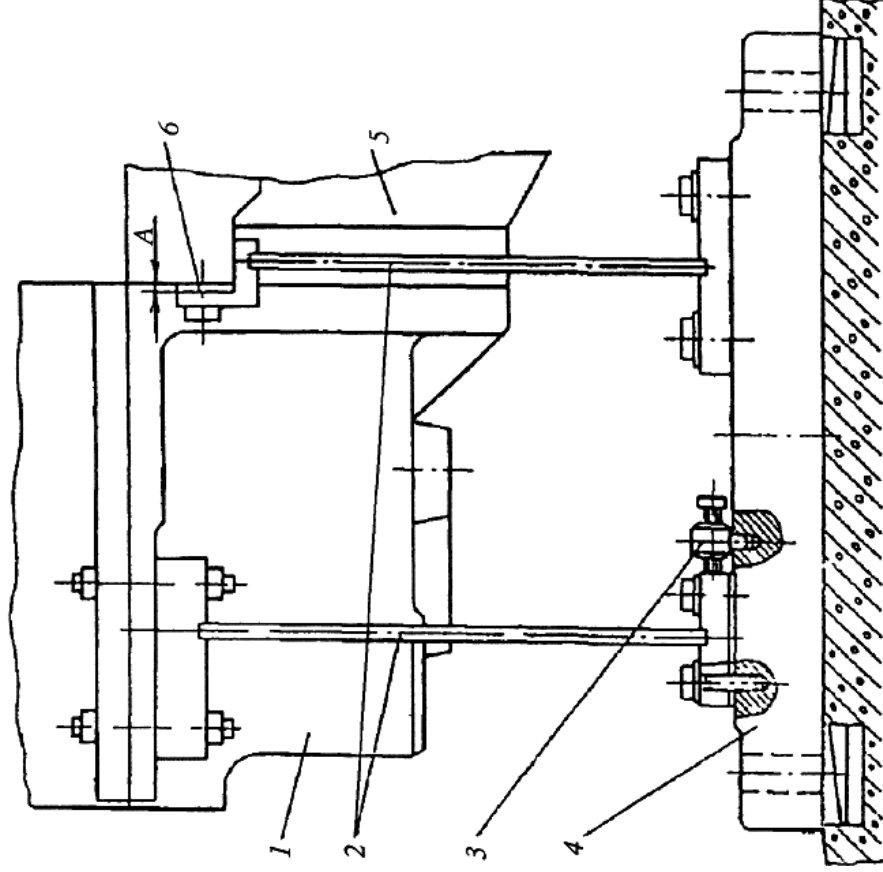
Схема расположения гибких опор конструкции КТЗ: 1 – корпус подшипника; 2 – гибкие опоры; 3 – приспособление для смещения опоры; 4 – фундаментная плита; 5 – цилиндр турбины; 6 – дистанционная прокладка; *A* – предварительный натяг гибкой опоры (дистанционная пластина)
